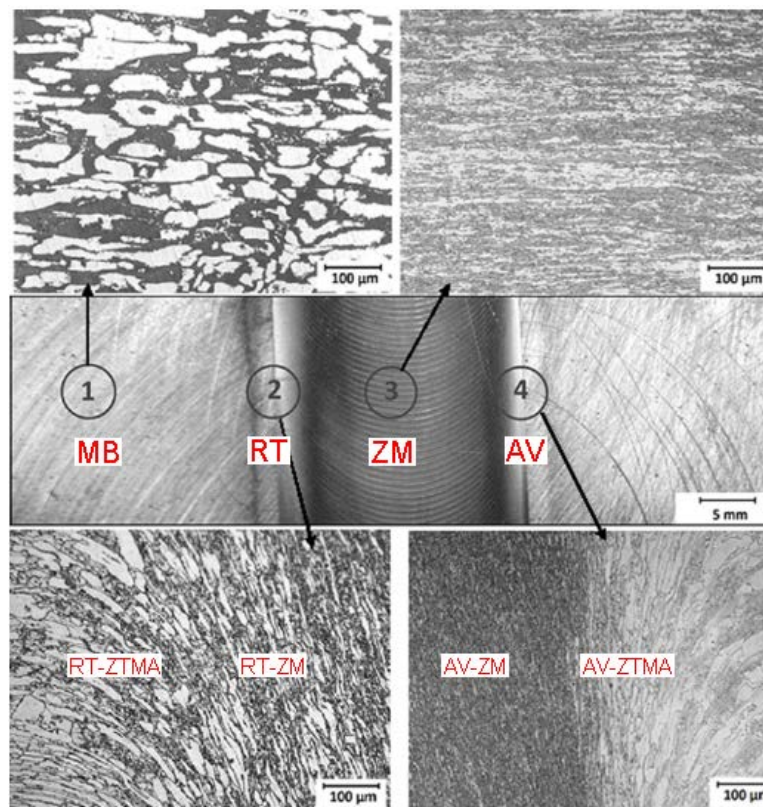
Macrografia da face e micrografia das diferentes regiões soldadas da liga UNS S82441 soldada por FSW (adaptado de [66]).
